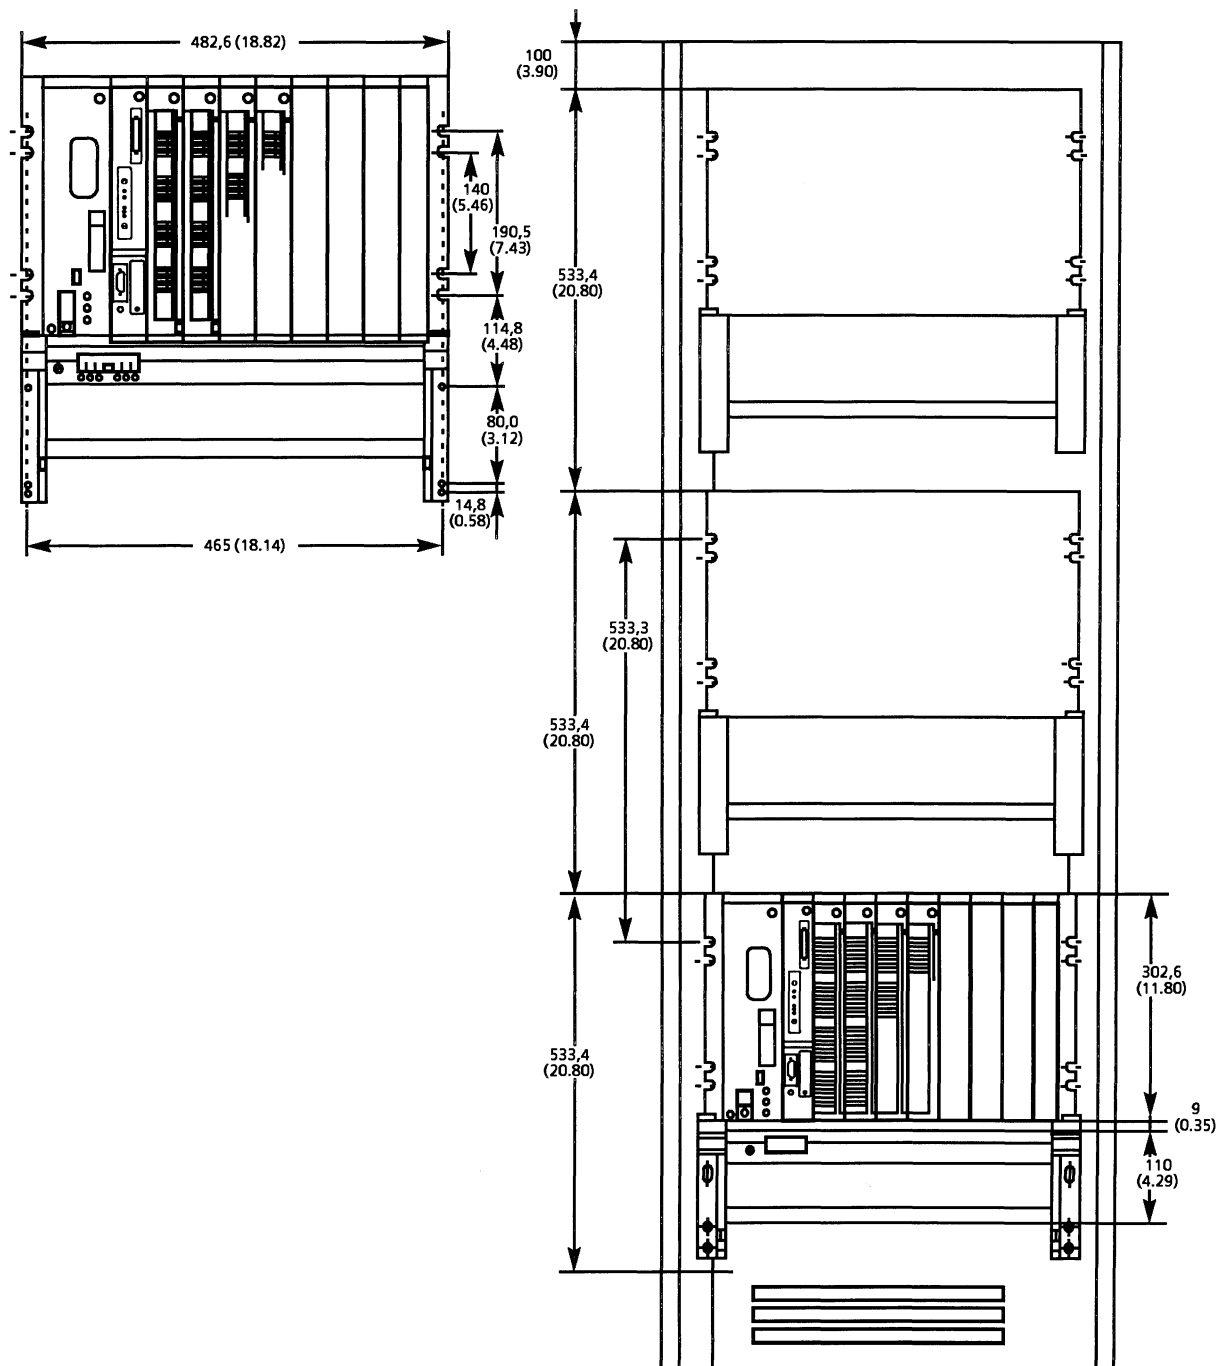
Bemaßung beim Einbau in 19"-Schränke
